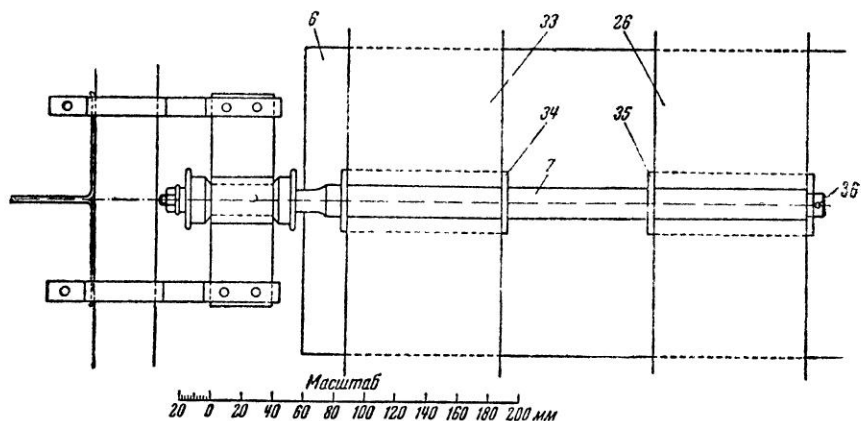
Крепление неподвижной оси ветроколеса к станине:
